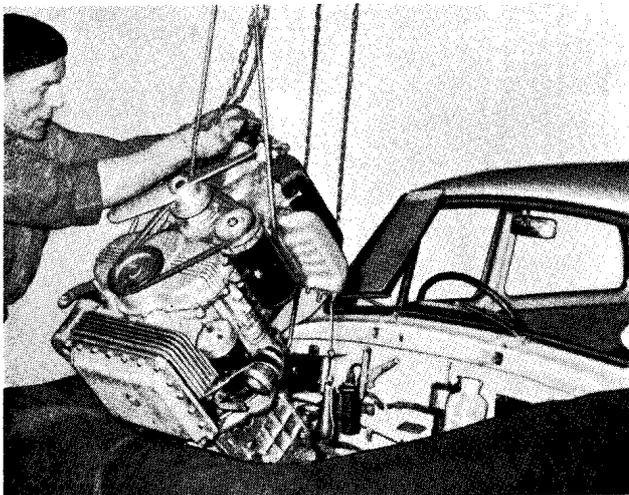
/19 - Sollevamento gruppo motore - frizione - cambio dalla vettura.
